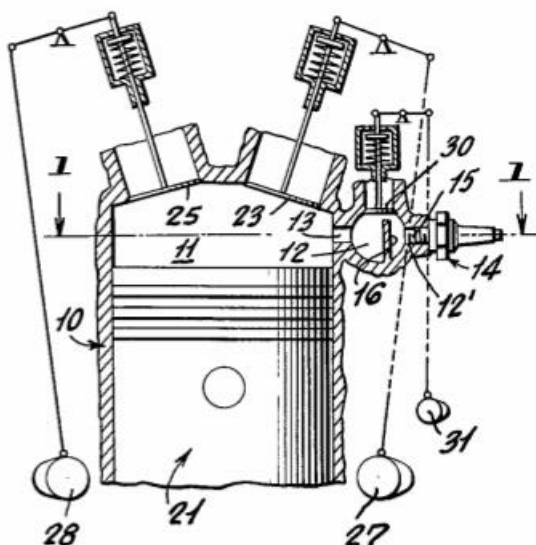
Design předkomůrky podle Harry Ricarda [2]
